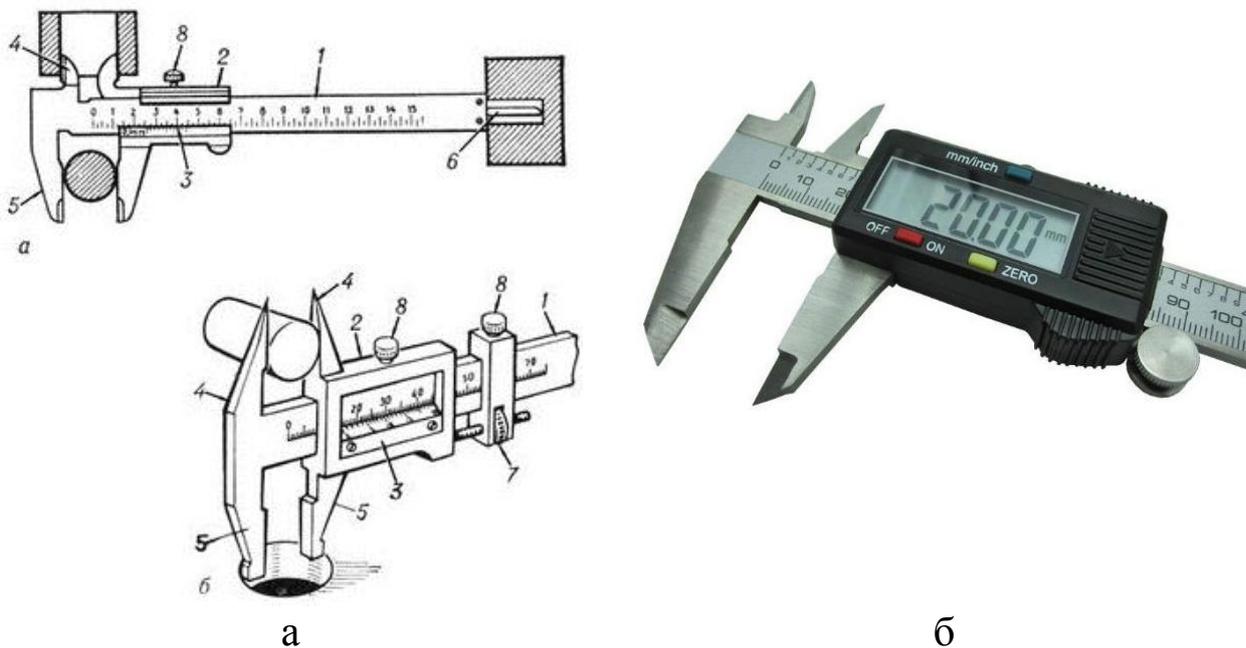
Штангенциркули: а – обычный: 1 – штанга; 2 – рамка; 3 – нониус; 4, 5 – губки для измерения диаметров (наружных и внутренних); 6 – линейка глубиномера; 7 – устройство для точного перемещения рамки; 8 – фиксирующий винт; б – цифровой
